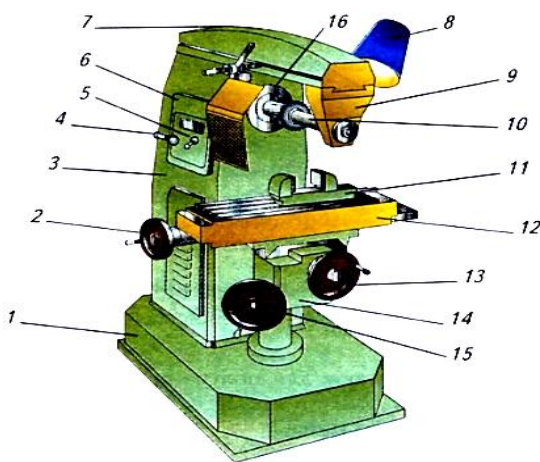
Устройство горизонтально-фрезерного станка НГФ-110Ш: 1 — основание; 2 — маховик продольной подачи; 3 — корпус станка; 4, 5 — рукоятки переключения частоты вращения шпинделя; 6 — коробка скоростей; 7 — хобот; 8 — светильник; 9 — серьга; 10 — оправка с фрезой; 11 — тиски; 12 — стол; 13 — маховик поперечной подачи; 14 — консоль; 15 — маховик вертикальной подачи; 16 — шпиндель
